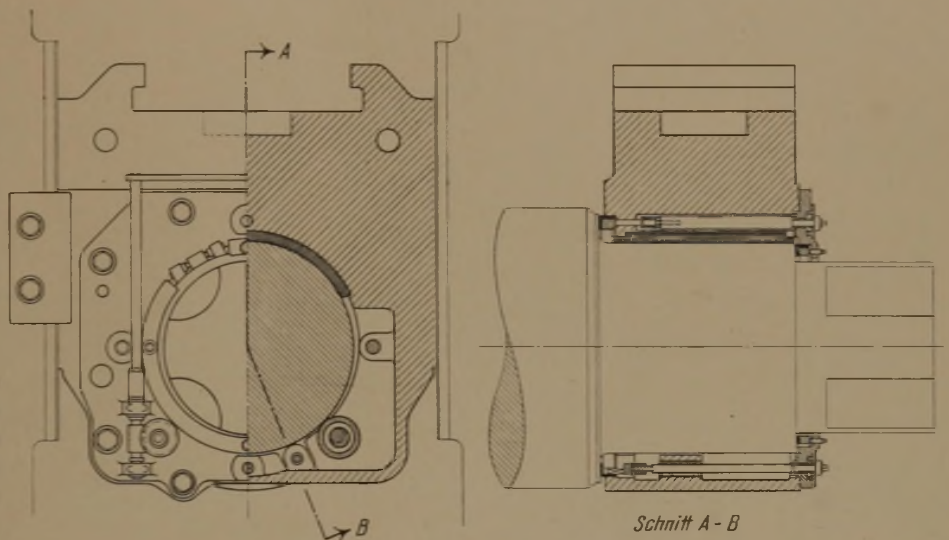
Geschlossenes Walzenlager mit Tragrollen.
